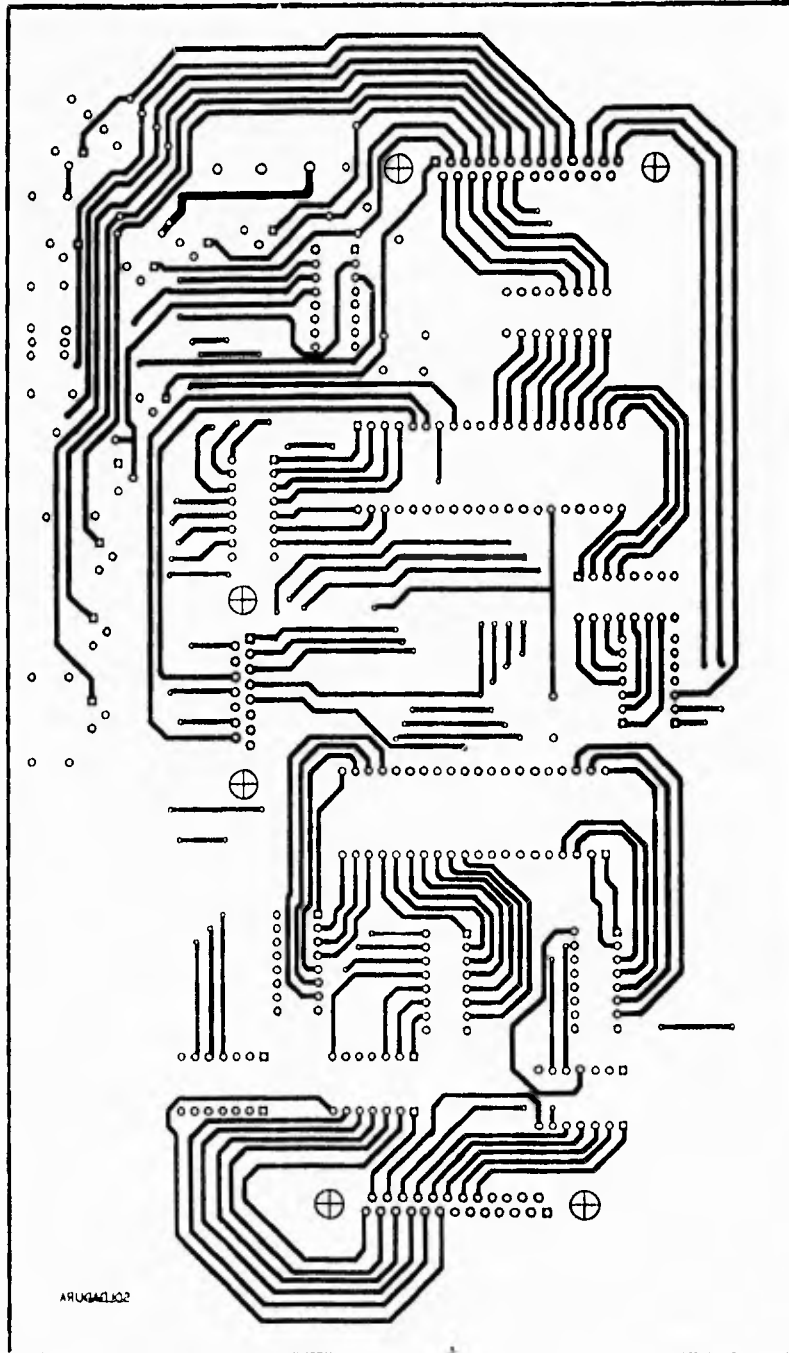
Cara de soldadura del circuito impreso de los driver's y de la etapa de potencia.
